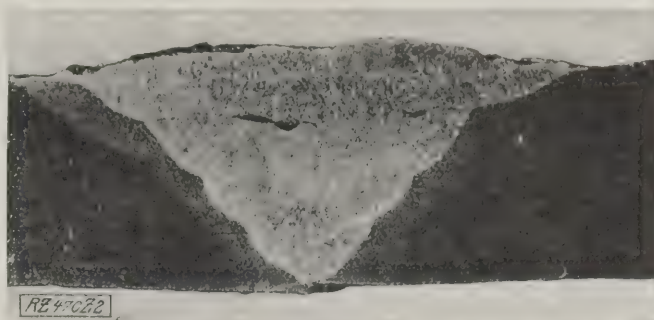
Querschnitt einer Schweißung. Helle Zone im Blech, Einzelschweißlagen; Schlackeneinschlüsse unter der obersten Lage; Gefügeunterschiede sind erkennbar, desgl. Einbrennwirkung des Lichtbogens in die Bleche ($\times 1,6$).
